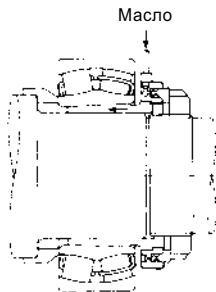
Посадка подшипника с помощью гидрогайки
